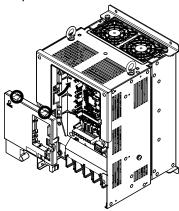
Réinstaller le couvert frontal (2A0110 à 2A0415 et 4A0058 à 4A1200)
